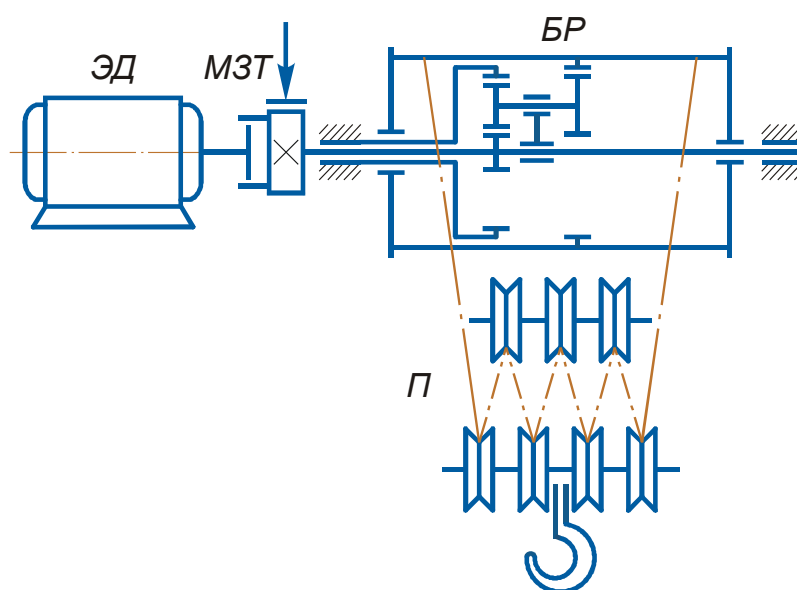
Кинематическая схема предлагаемого механизма: ЭД — электродвигатель; МЗТ — муфта зубчатая с тормозным шкивом; БР — барабан-редуктор; П — полиспаст с крюковой подвеской
